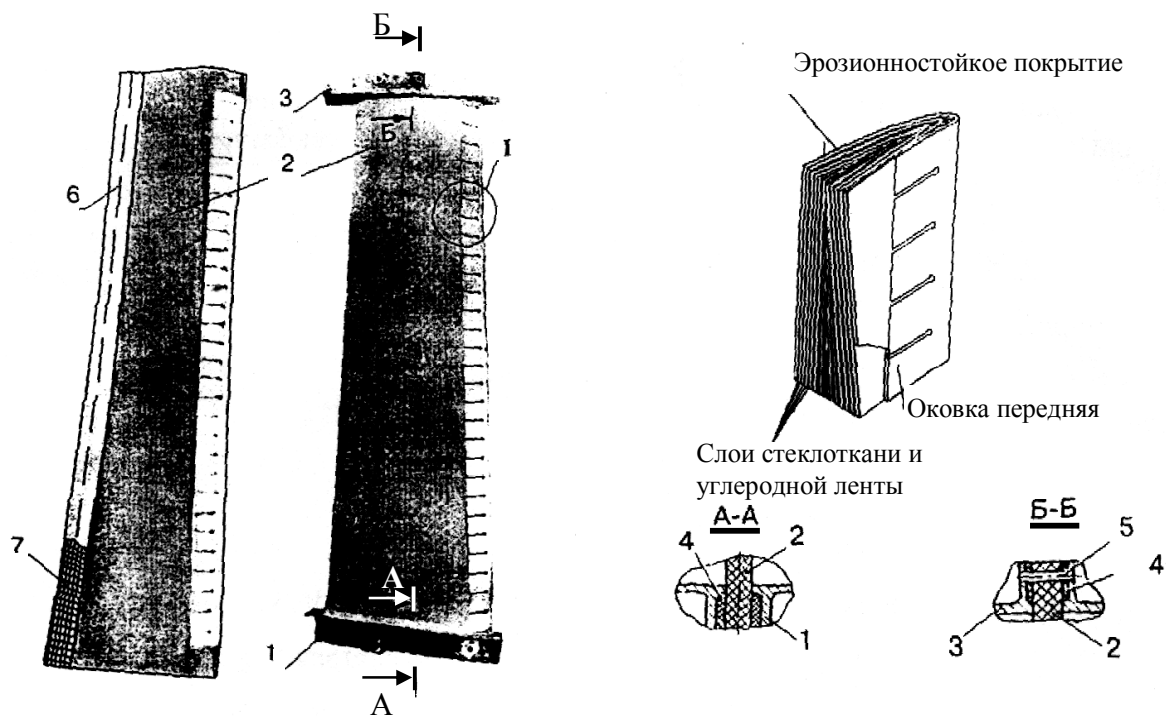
Лопатка спрямляющего аппарата вентилятора двигателя Д-18Т: 1, 3 – верхняя и нижняя полки; 2 – перо из углестеклопластика; 4 – полимерный наполнитель; 5 – штифт; 6 – прошивка нитью СВМ; 7 – сетка никелевая
